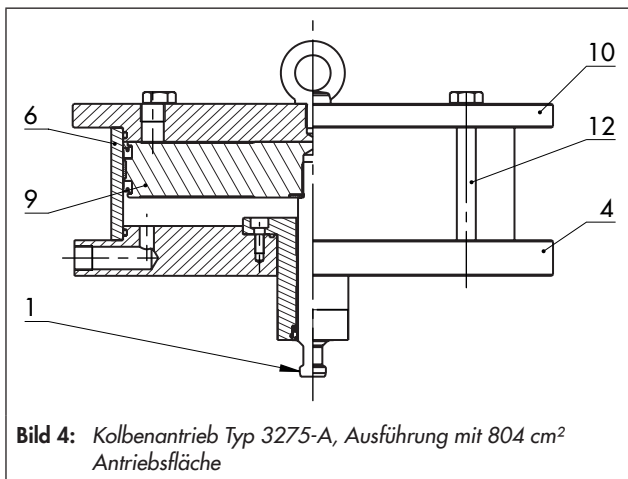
Kolbenantrieb Typ 3275-A, Ausführung mit 804 cm² Antriebsfläche
